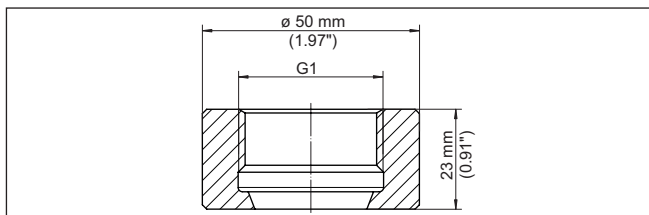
Dimensions raccord à souder G1 (ISO 228-1) - joint conique
